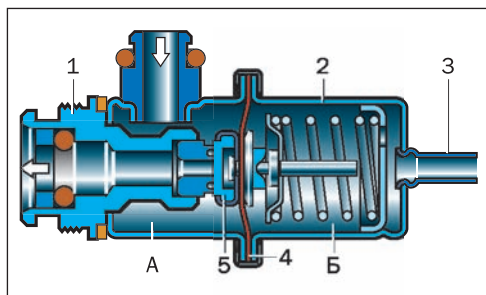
Регулятор давления топлива: 1 — корпус; 2 — крышка; 3 — патрубок для вакуумного шланга; 4 — мембрана; 5 — клапан; А — топливная полость; Б — вакуумная полость
